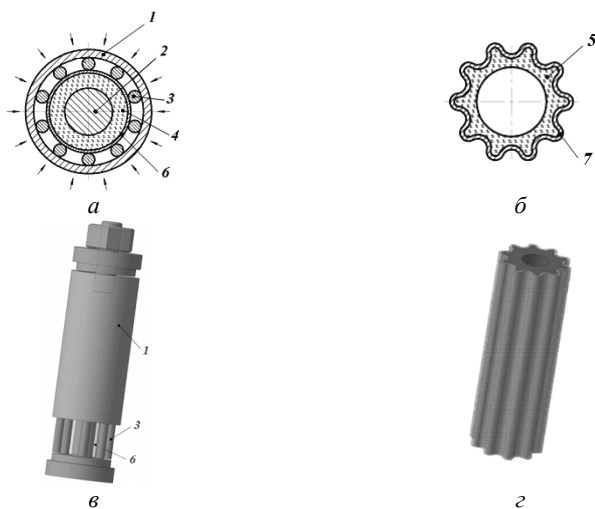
Оснастка для изготовления композиционного ФЭ по третьему варианту: а – сечение оснастки; б – сечение композиционного ФЭ; в – общий вид оснастки; з – общий вид прессовки композиционного ФЭ
